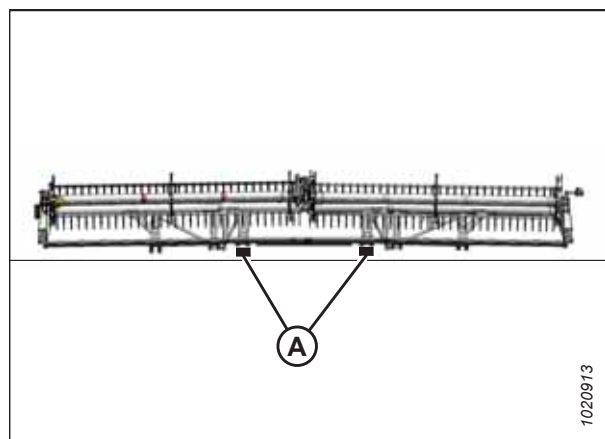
FlexDraper®-blokplaceringer – dobbelt vinde
